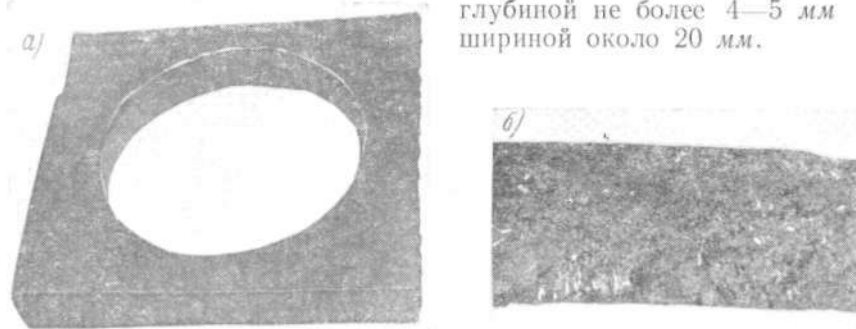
Внешний вид реза при кислородно-флюсовой резке: а — заготовка из листа толщиной 20 мм; б — кромка толщиной 40 мм.
